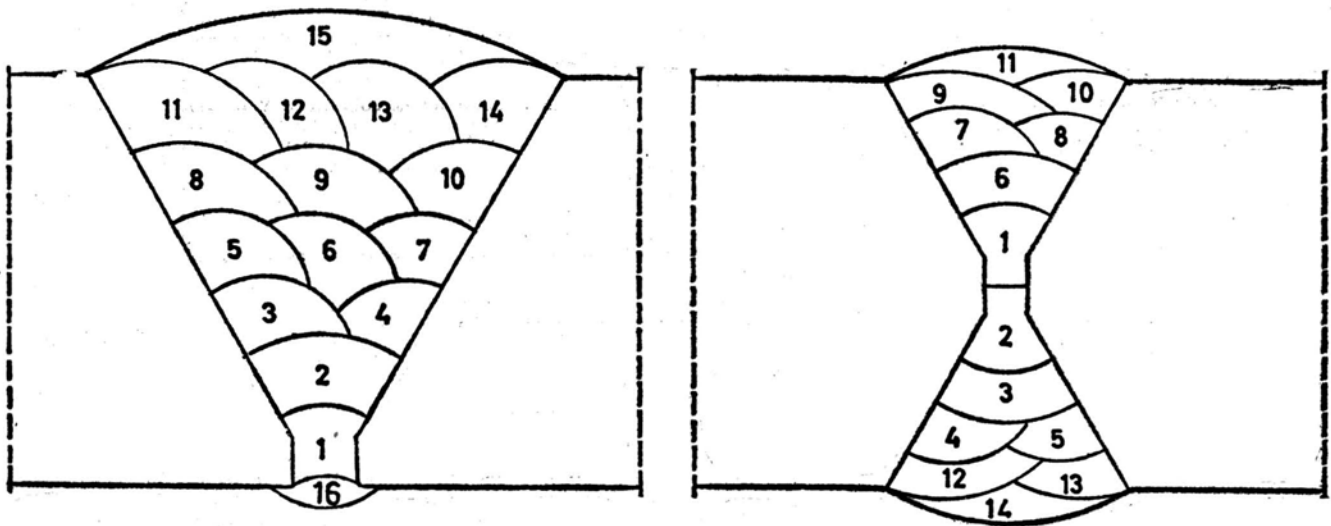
SOLDADURAS DE VARIOS CORDONES
